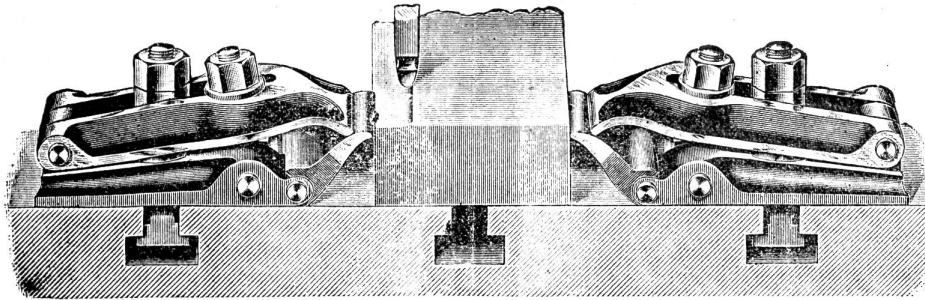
Im Gebrauch auf der Hobelmaschine.
